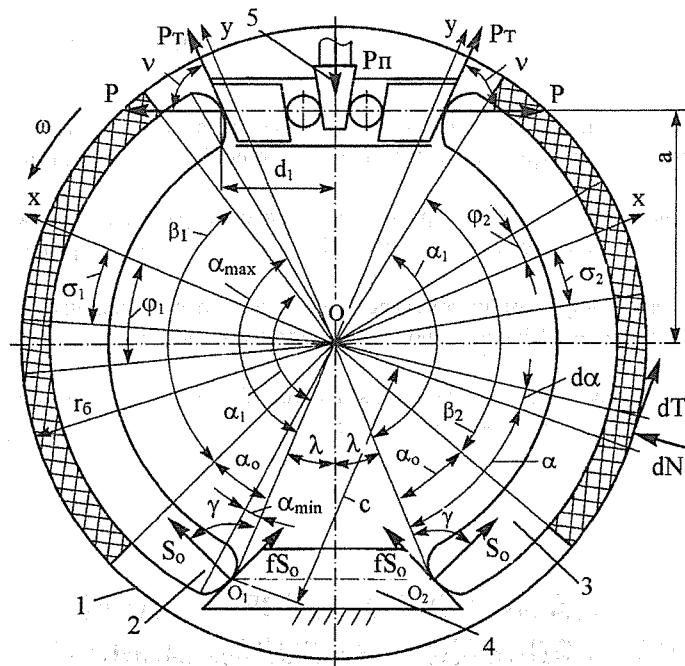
Розрахункова схема барабанно-колодкового гальмаз малим самопідсиленням, плаваючими колодками клиновим приводом
